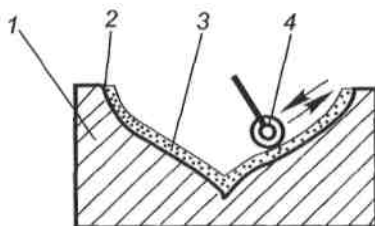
Схема контактного формування: 1 – форма; 2 – роздільний шар; 3 – склотканина; 4 – ролик
